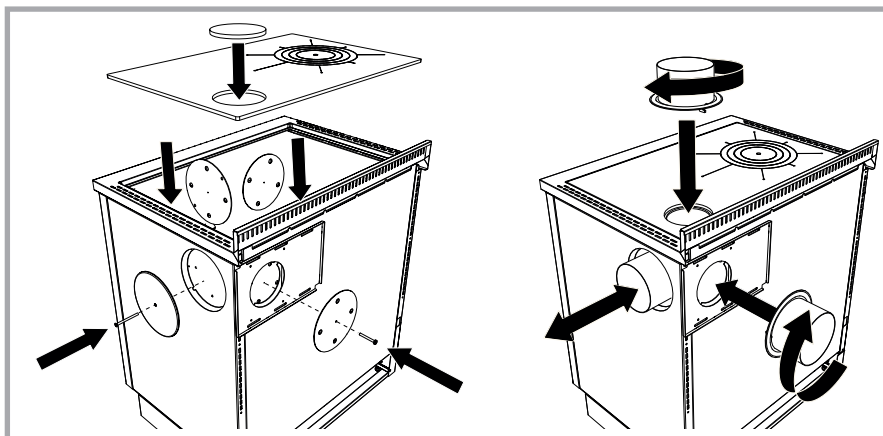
Mehrfachanschluss mit Backofen, korrekte Vorbereitung für den Anschluss.
